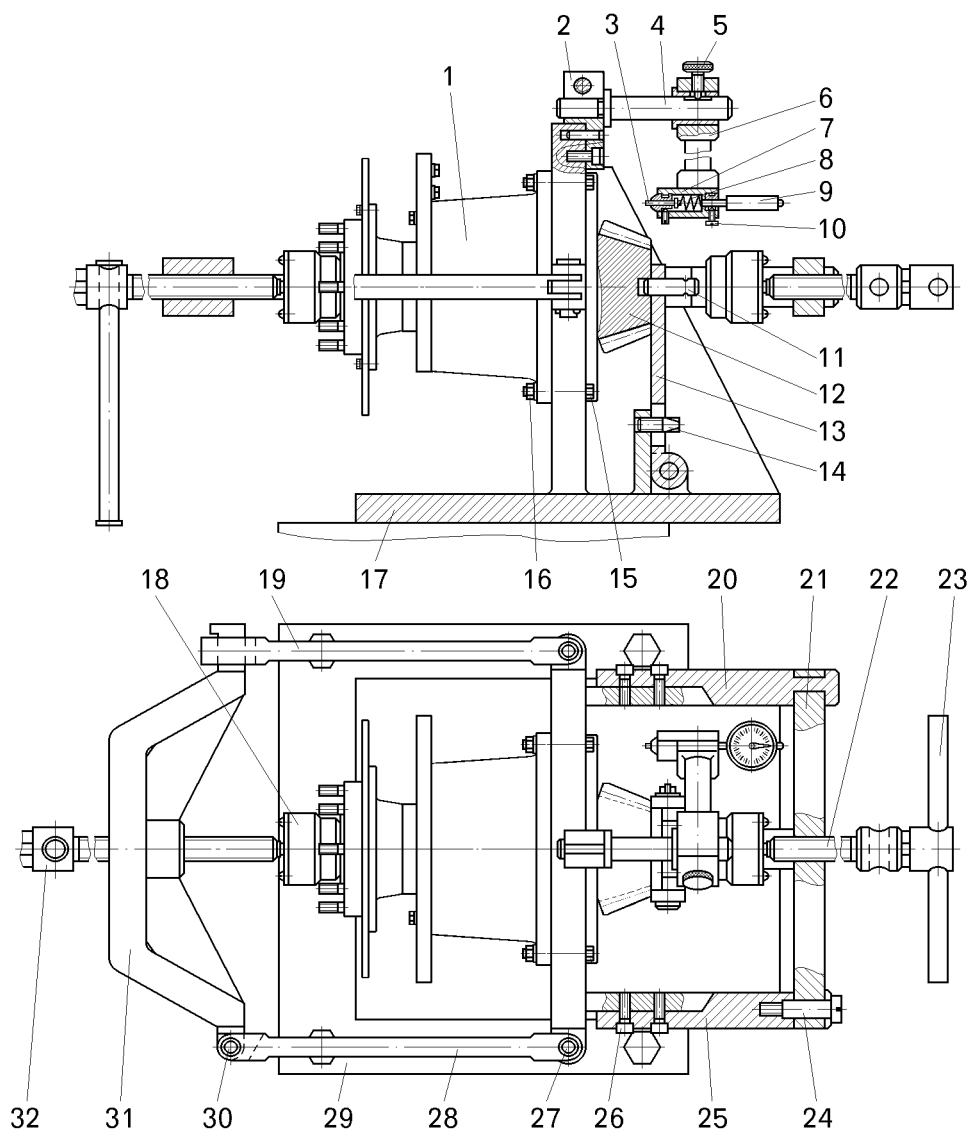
Стенд для разборки, сборки и регулировки зазора ведущей шестерни:
